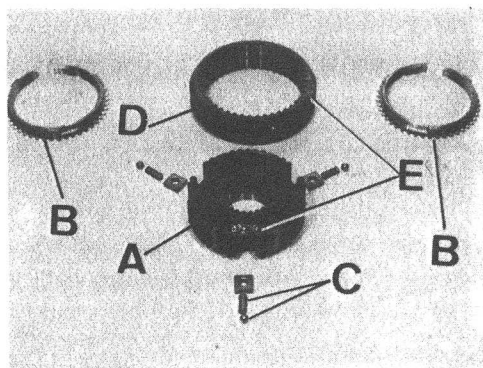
Conjunto sincronizador 3a y 4a V.
